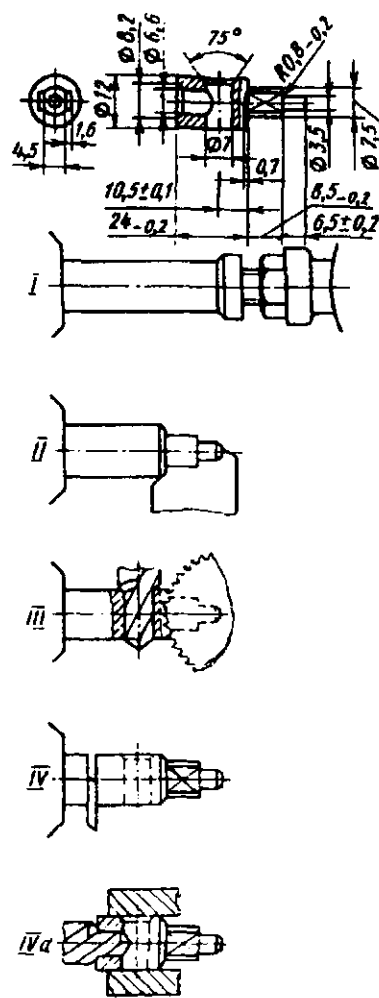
Наладка одношпиндельного токарно-револьверного автомата для полной механической обработки детали, включая "доделочные" операции
